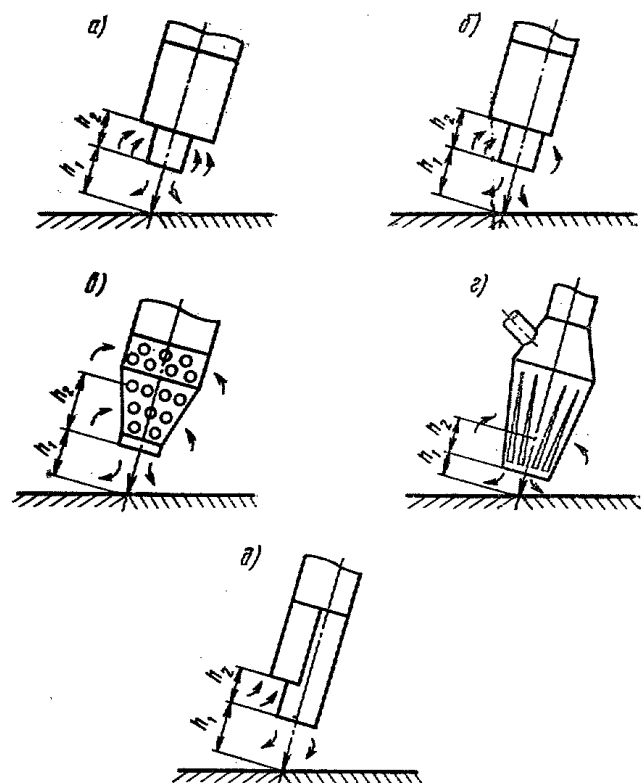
Воздухоприемники к горелкам сварочных полуавтоматов:
